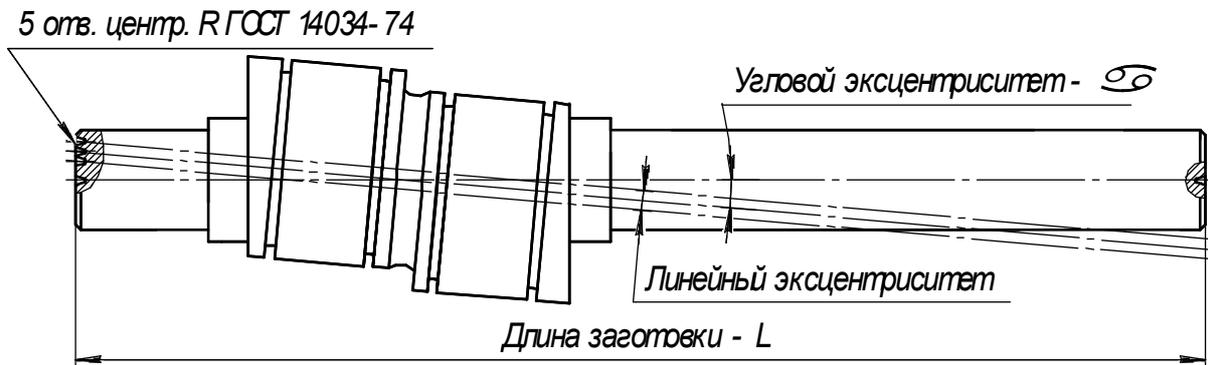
Эксцентриковый вал волнового передаточного механизма с промежуточными телами качения
